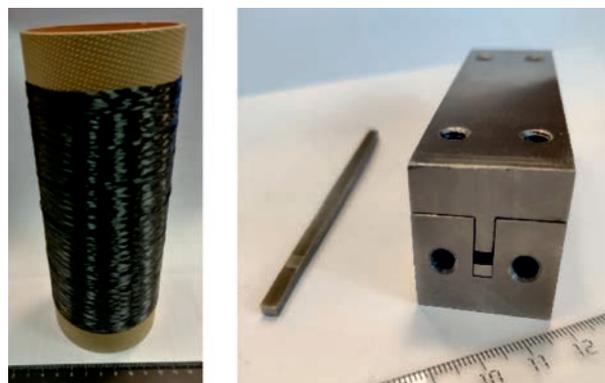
Волокна SiC и оснастка для изготовления образцов
